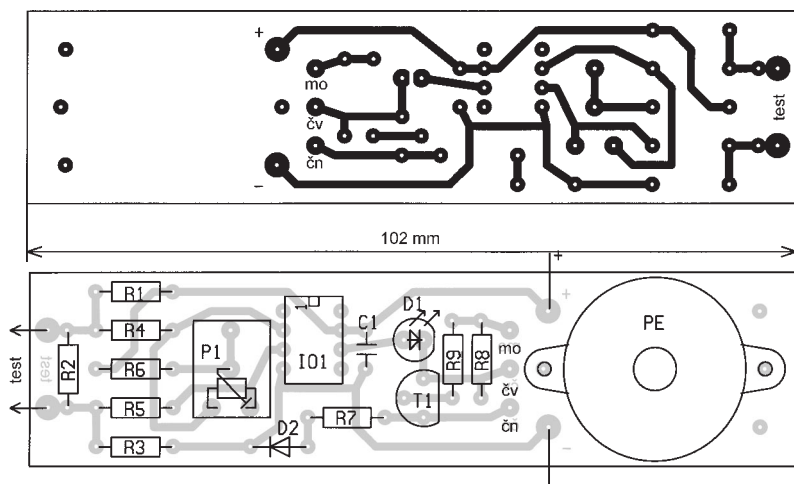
Deska s plošnými spoji pro zkoušečku a rozmístění součástek
